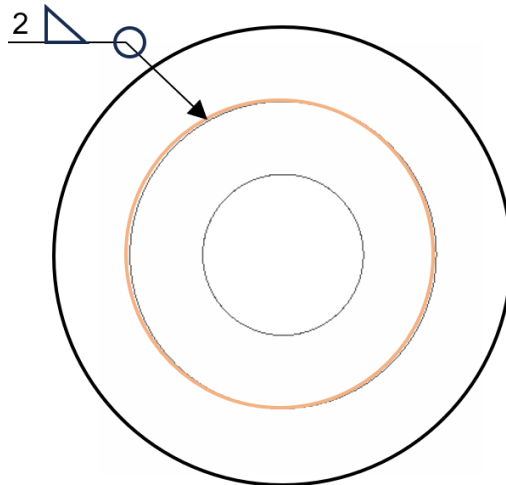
Esquema de soldadura entre cubo y anillo inferior del rodete, dimensiones en mm.
